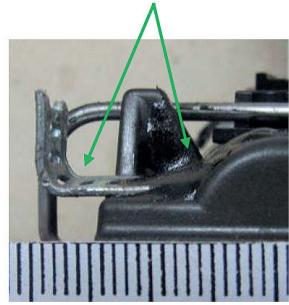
Загальний вигляд внутрішніх поверхонь та механізмів лічильника газу «Ельстер G4» і місця розташування металевої пластини з нашаруванням полімерної речовини чорного кольору (вигляд збоку)
